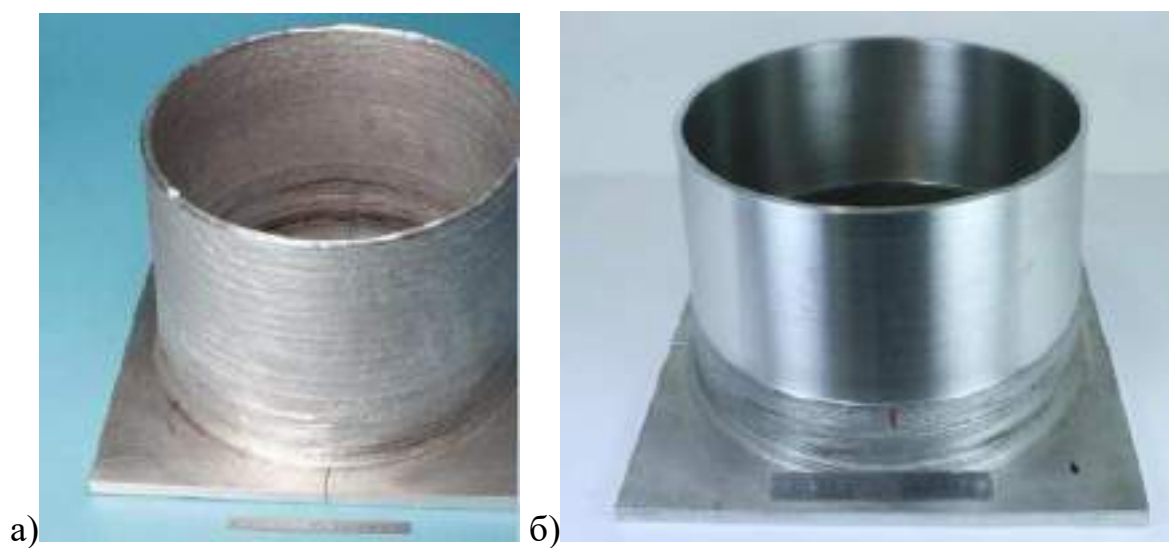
Виготовлення циліндричної деталі супутника з алюмінієвих сплавів із змінною товщиною стінки (час виготовлення – 6 годин) [20]: а) – після пошарового нарощування; б) – після механічної обробки.
